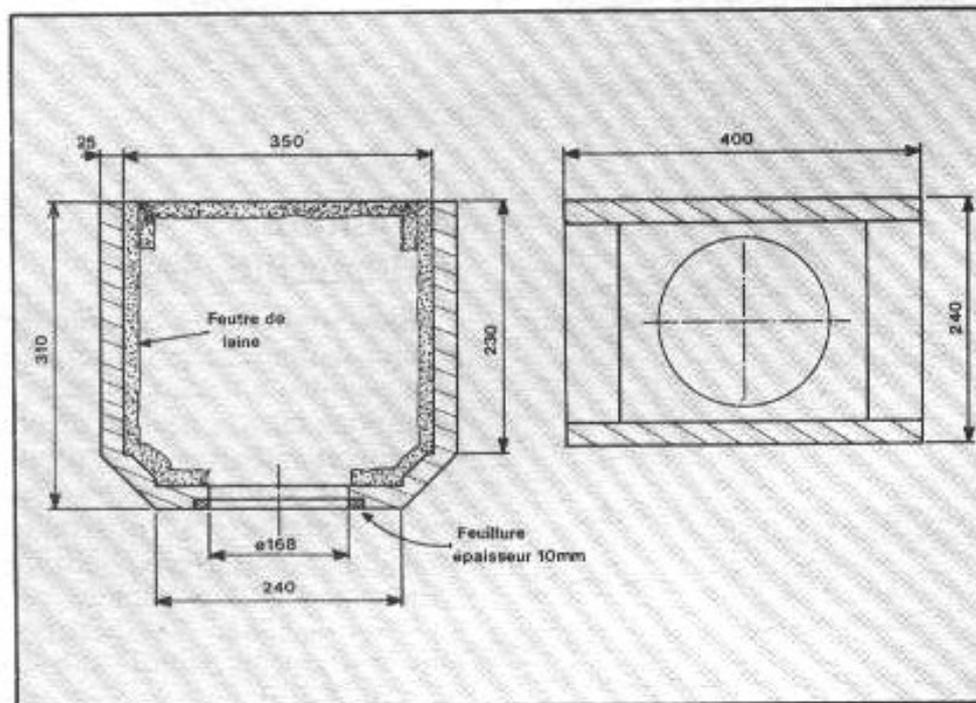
Plan du coffret médium. Il est réalisé également en médite de 25 mm. L'ensemble des parois est recouvert de feutre de 10 mm. Un rideau amortit l'onde arrière.
